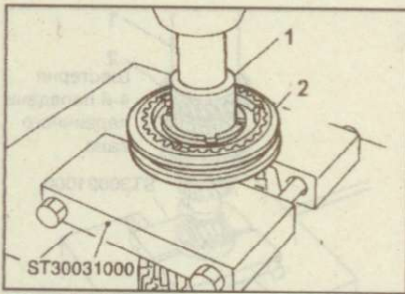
Выпрессовка втулки (1) шестерни заднего хода и синхронизатора (2) 5-й передачи и передачи заднего хода
